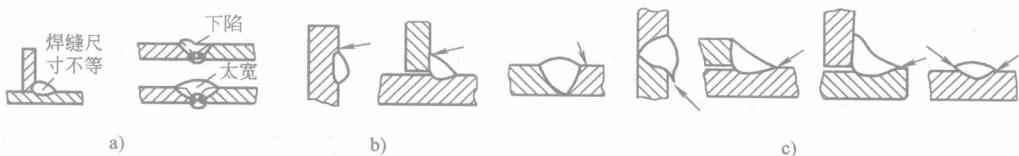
焊接电流过大容易产生的焊接缺陷
